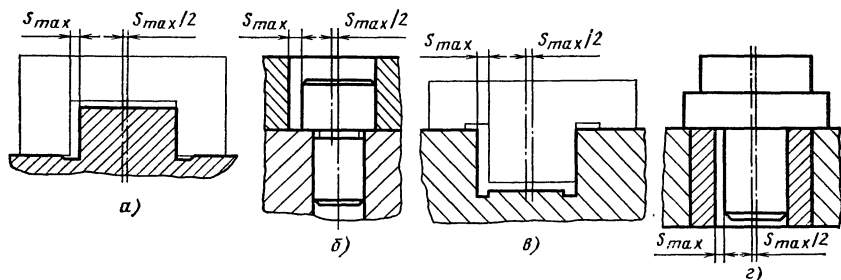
Схемы установки заготовки: по охватывающей поверхности на выступ (а) и на палец (б); по охватываемой поверхности в паз (в) и в отверстие втулки (г)
